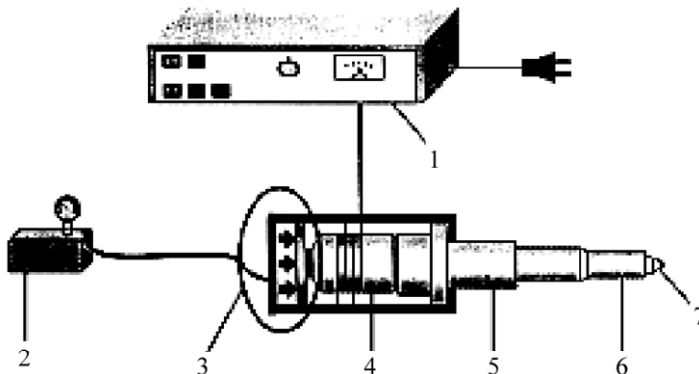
Схема установки для УЗО: 1 – ультразвуковой генератор; 2 – воздушный компрессор для обеспечения статической нагрузки на инструмент; 3 – механизм регулировки усилия, обеспечиваемого пневмосистемой; 4 – пьезо- или магнитострикционный преобразователь; 5 – бустер; 6 – волновод; 7 – рабочий инструмент
